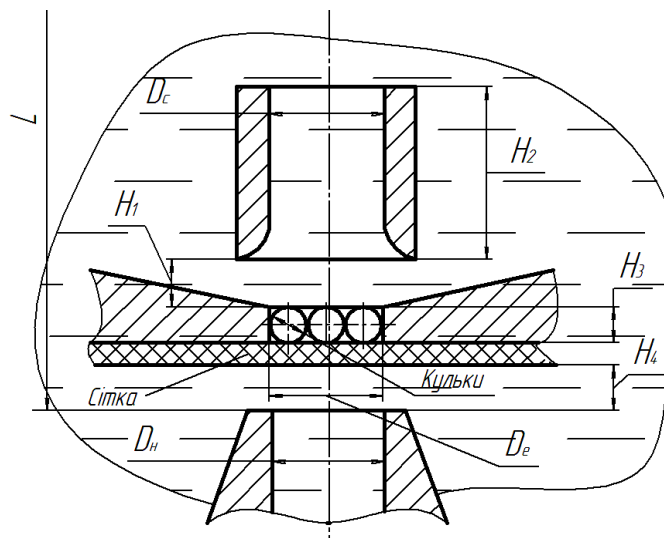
Конструктивна схема сопла з ежектором для створення двофазного потоку рідини затопленого струменя з твердими частинками:
